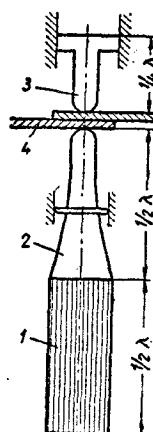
用与焊接表面垂直的传振杆使焊件产生超声振动的原理图：
